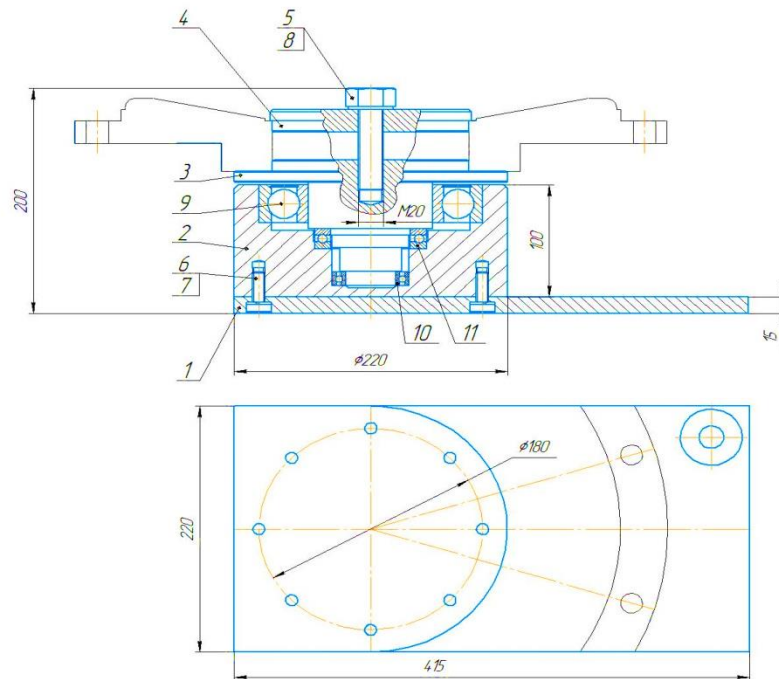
Универсальное контрольно-измерительное приспособление для контроля радиального и торцевого биений детали :
